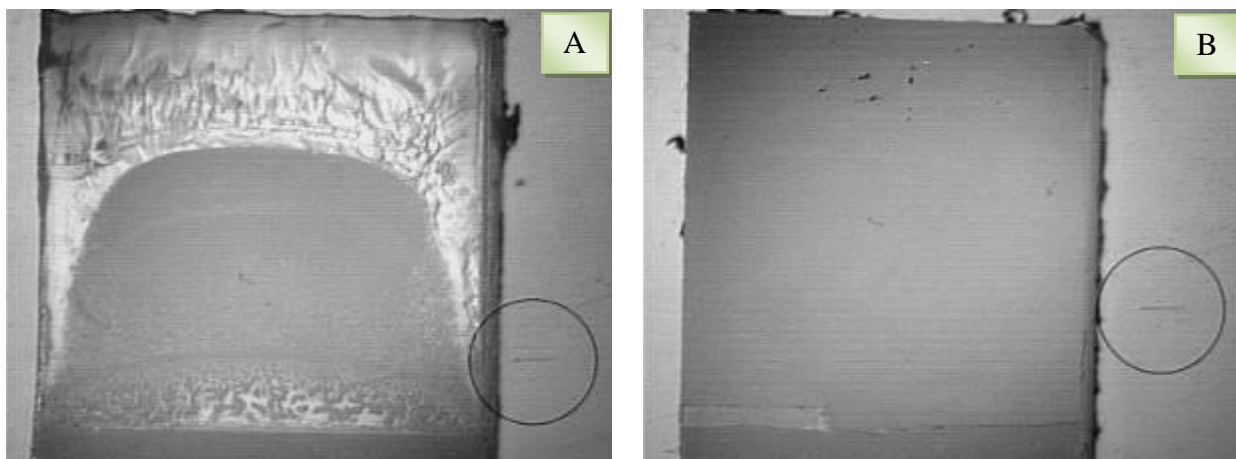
Superficie de fractura. A) HDPE; B) W-HDPE. Fractura ~ 0 °C.
